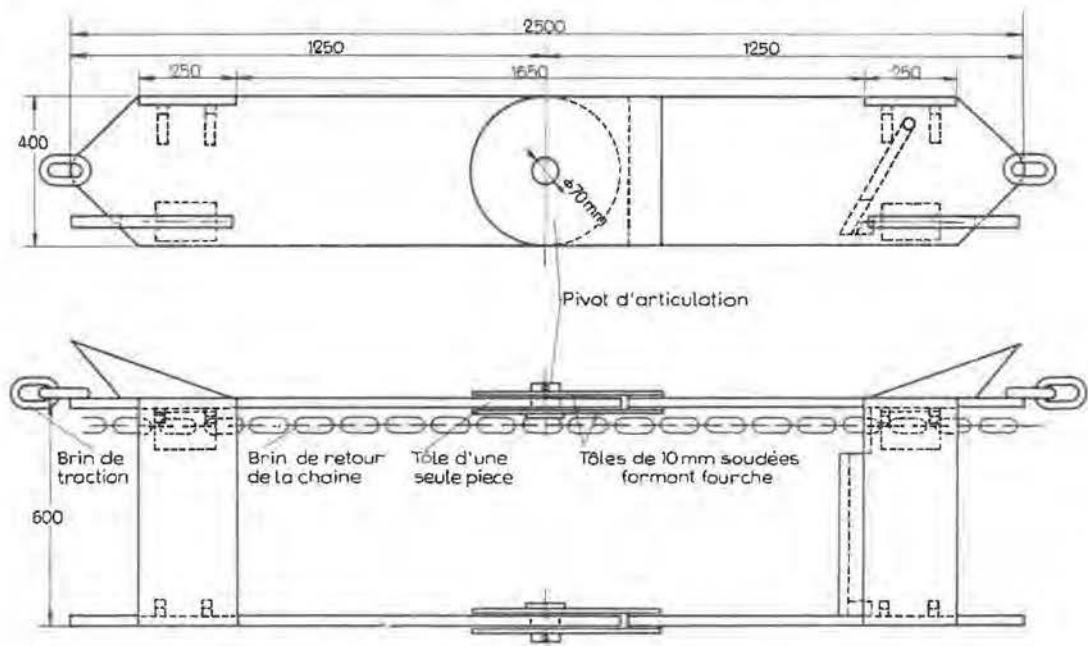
Caisse de scraper à simple élément, les co-taux sont soudés sur la paroi frontale.
